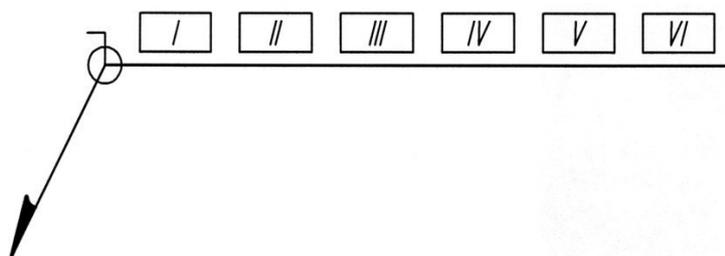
Полное условное обозначение сварного шва
